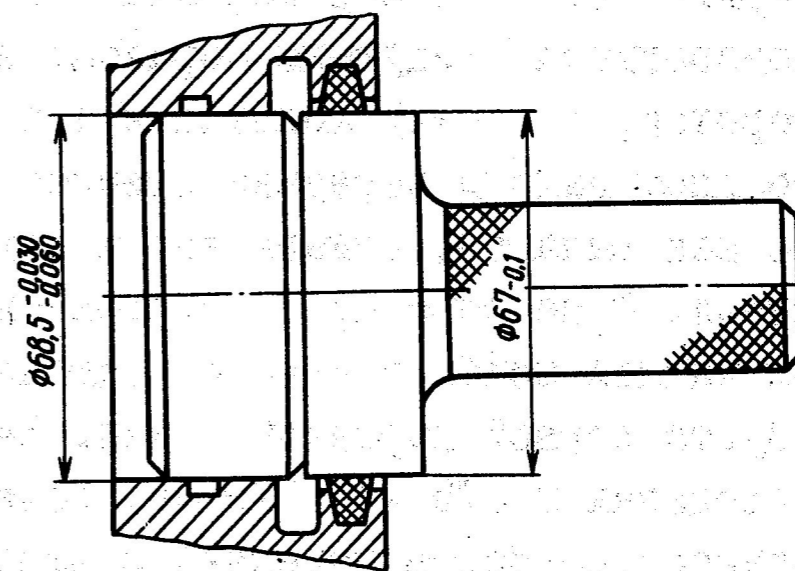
Оправка 5-У-27678 для обжима сальника коленчатого вала
